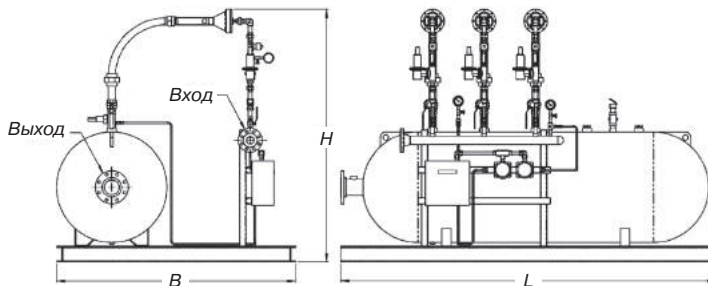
Габаритные размеры установки смесительной Metan-3-3-600(-3000)-B
